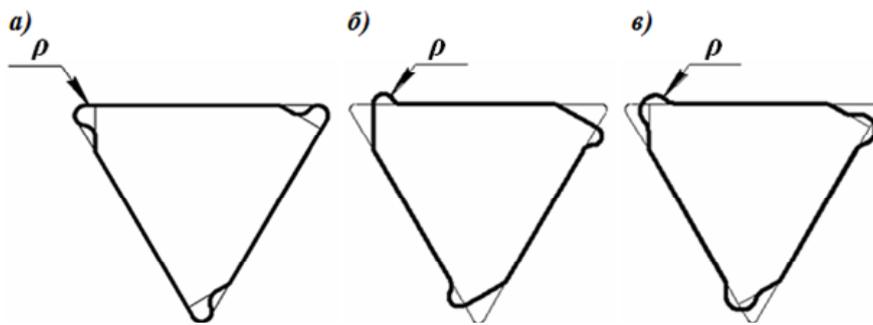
Формирование дополнительных выступов радиуса ρ на заготовках трехгранных БМНП: а) на лыске, б) на боковой поверхности, в) с обеих сторон режущей кромки.
